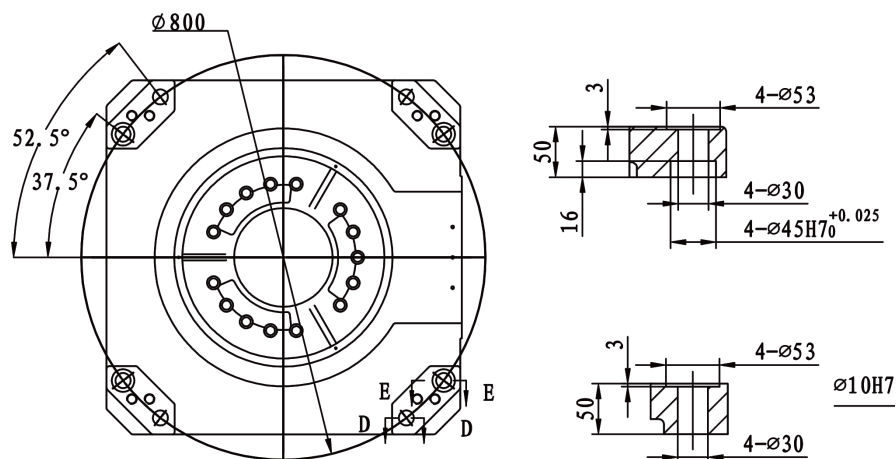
Габаритные чертежи робота-манипулятора SD7-900.
